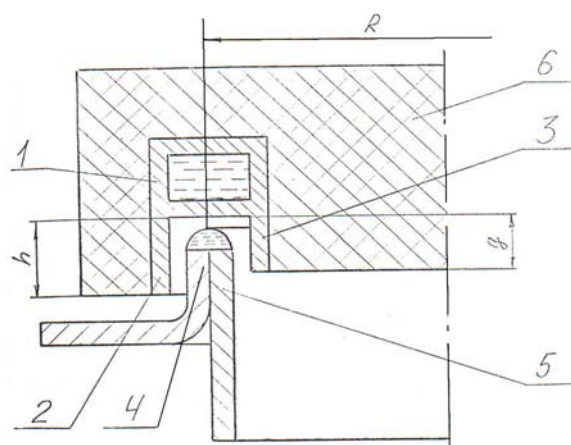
Индуктор для высокочастотной сварки
